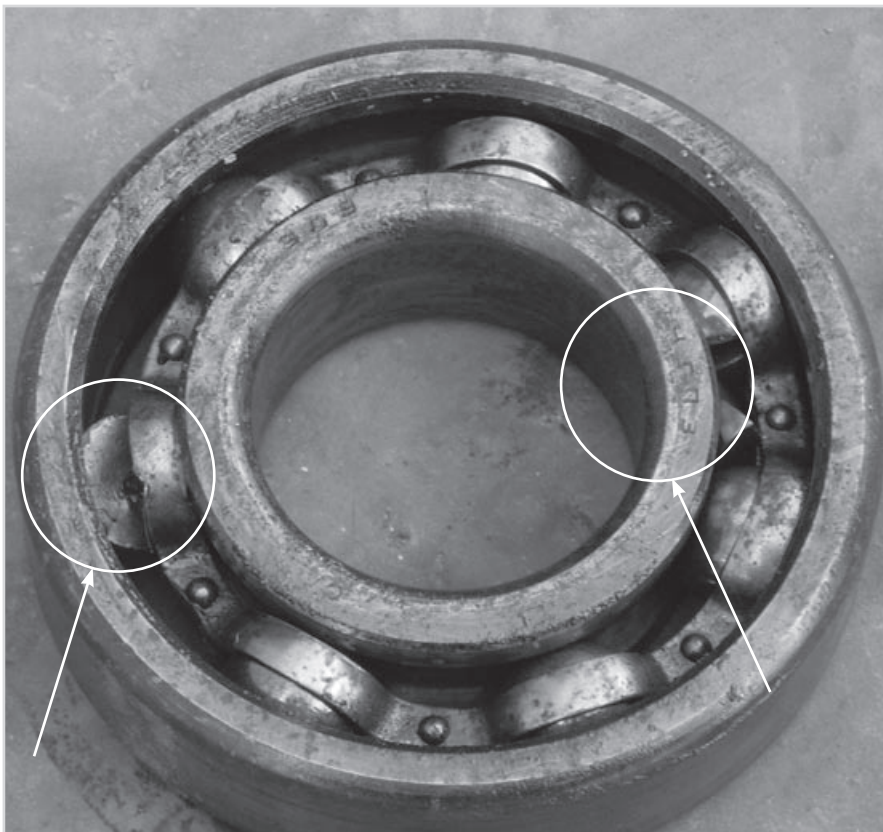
Разрушенный на две части шарик в обойме подшипника
